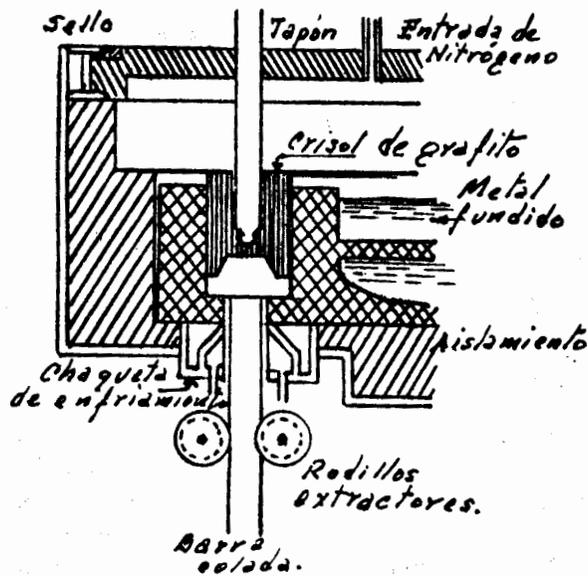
MAQUINA DE COLADA CONTINUA DE MOLDE RECIPROCANTE.
